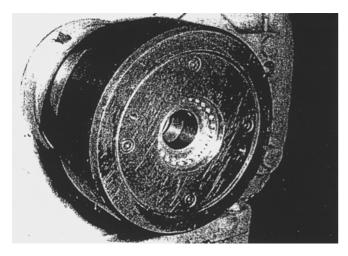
Установка зубчатого колеса 3-й передачи вторичного вала КП и первичного вала в приспособлении для накатывания боковых поверхностей зуба на токарном станке
